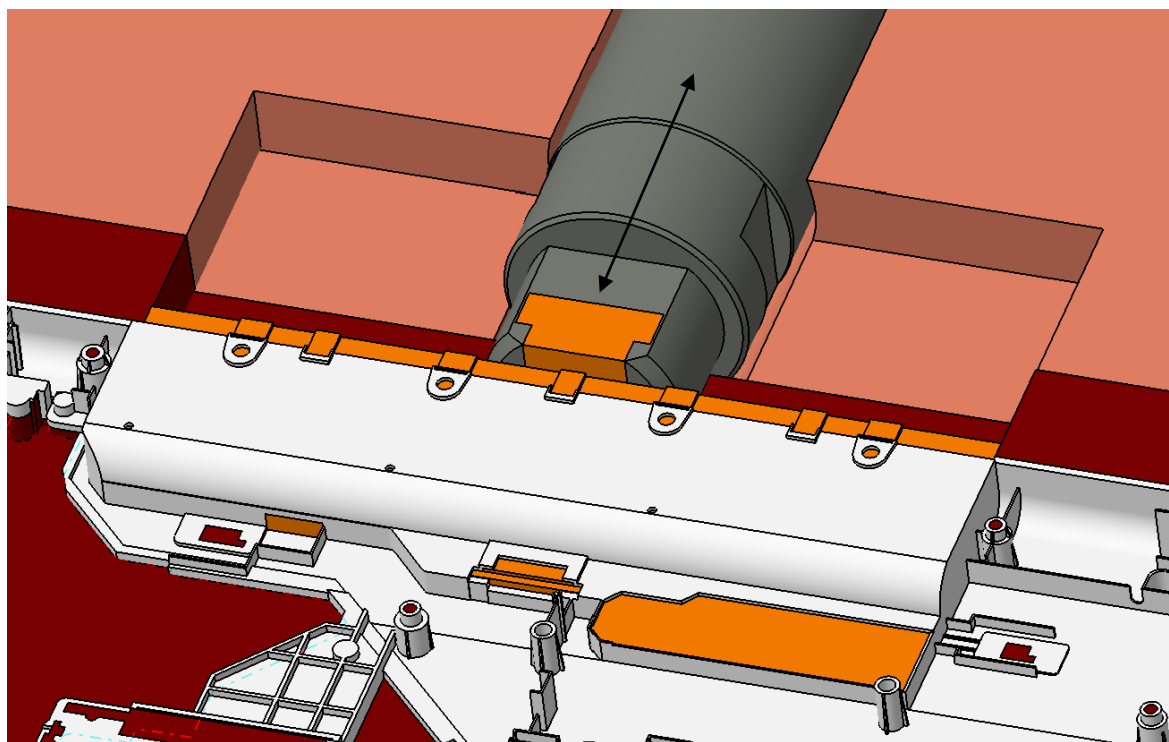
Boční odformování pro SD kartu a porty pro sluchátka
